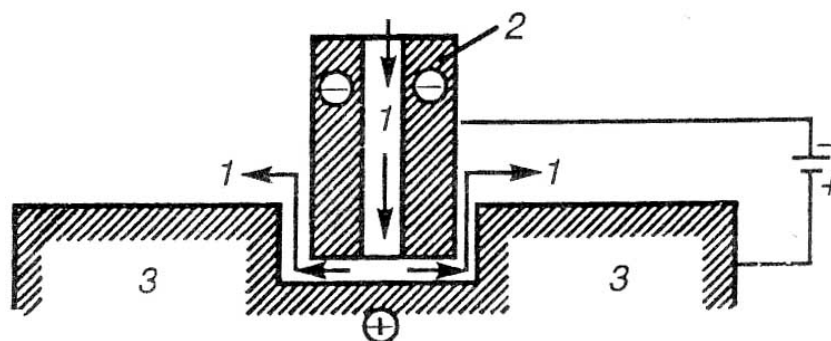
Схема станка для электрохимического удаления металла. 1 – раствор электролита; 2 – катод-инструмент; 3 – анод-заготовка.
